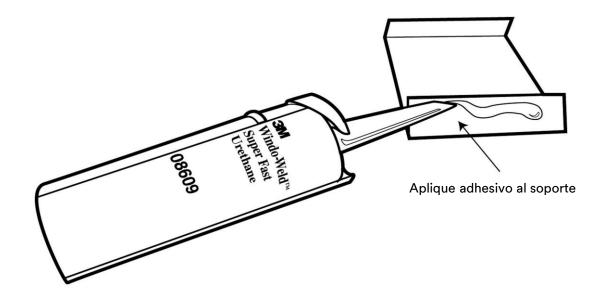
Aplicación de uretano 3M Windo-Weld Super Fast al soporte 3M.
